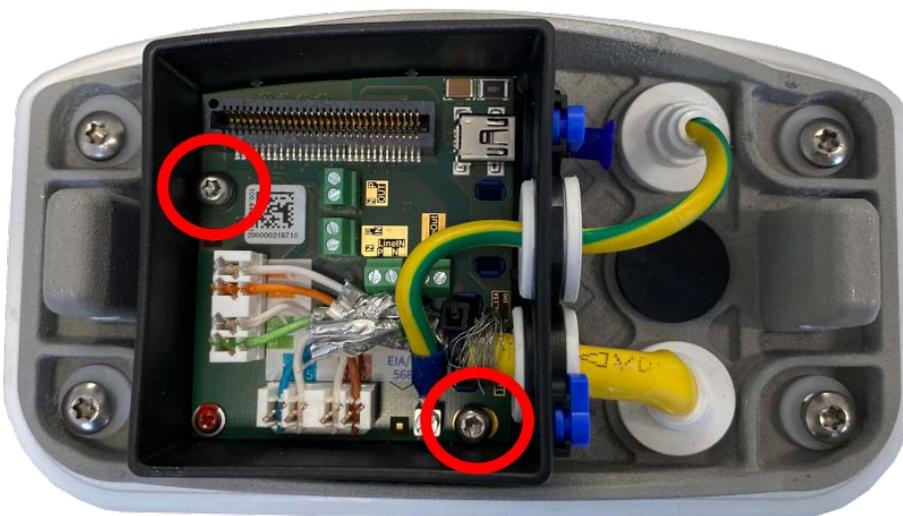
Anschlussbox LSA (Draufsicht) mit zwei Schrauben (rot hervorgehoben) an Montageplatte montieren
